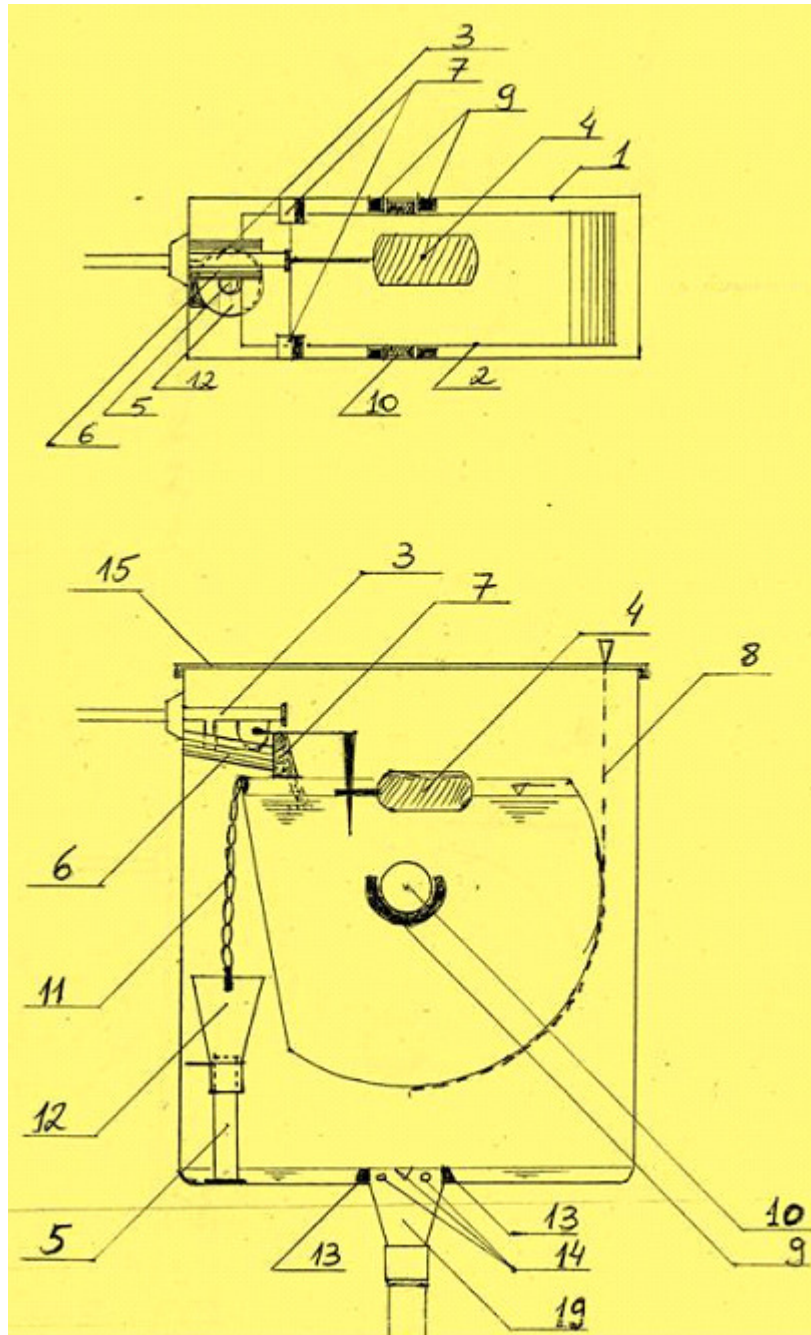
Planta e Perfil da Caixa de Descarga Econômica
